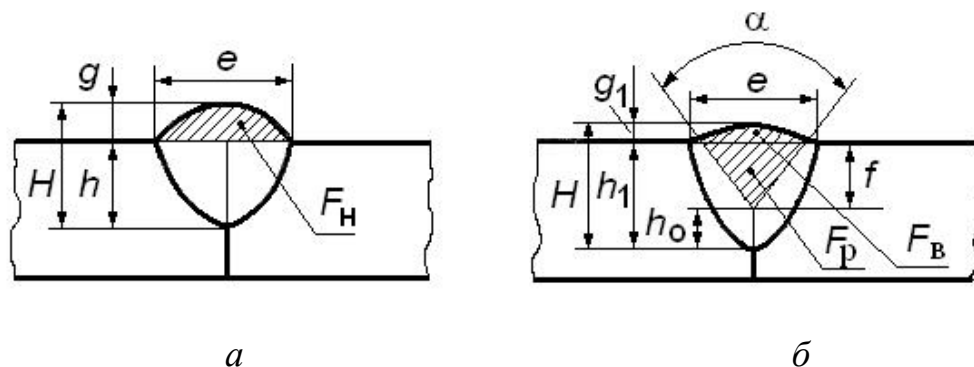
Размеры швов, выполненных на одном режиме при сварке без зазора и разделки (а) и при сварке в разделку (б)
